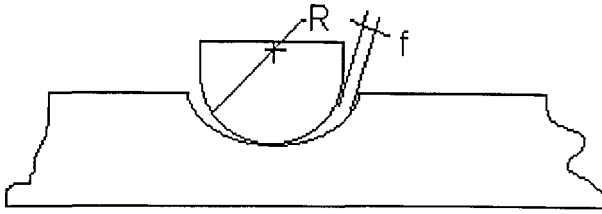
Esquema de usinagem com avanço da ferramenta perpendicular a geratriz do entalhe
